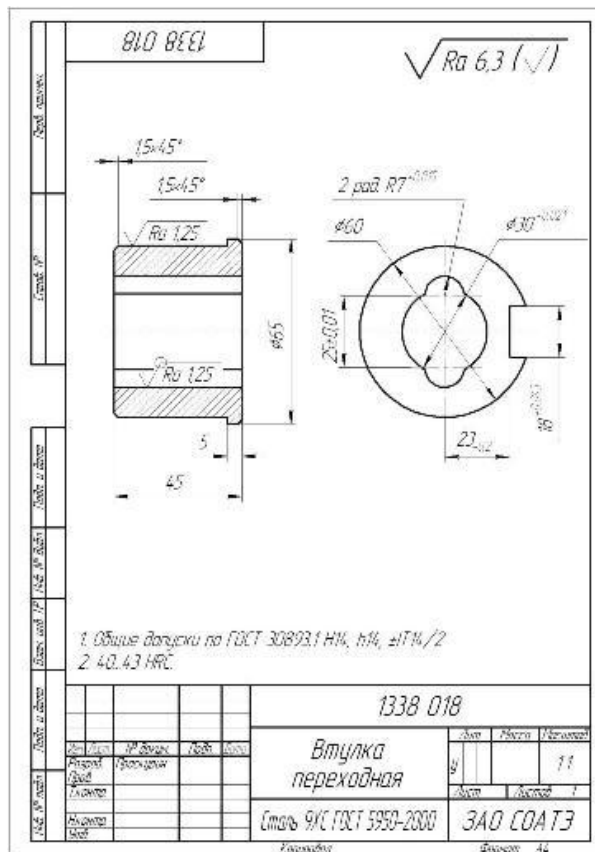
Деталь испытательного стенда. Втулка переходная
